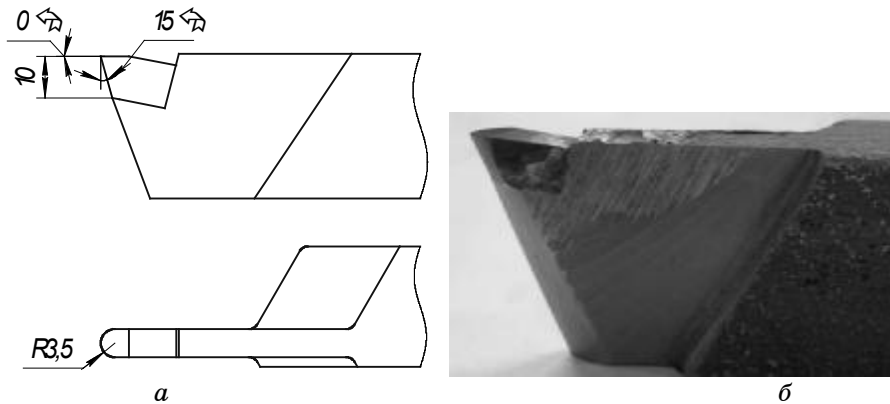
Эскиз (а) и фотография (б) резца с напайной пластиной из твердого сплава ВК8
